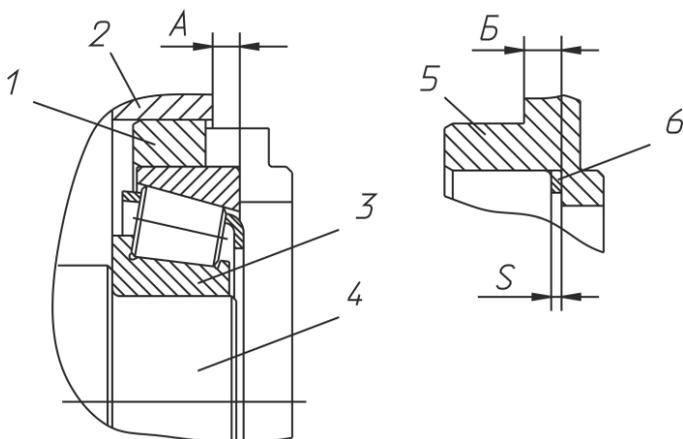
Регулировка осевого зазора в подшипниках промежуточного вала:
